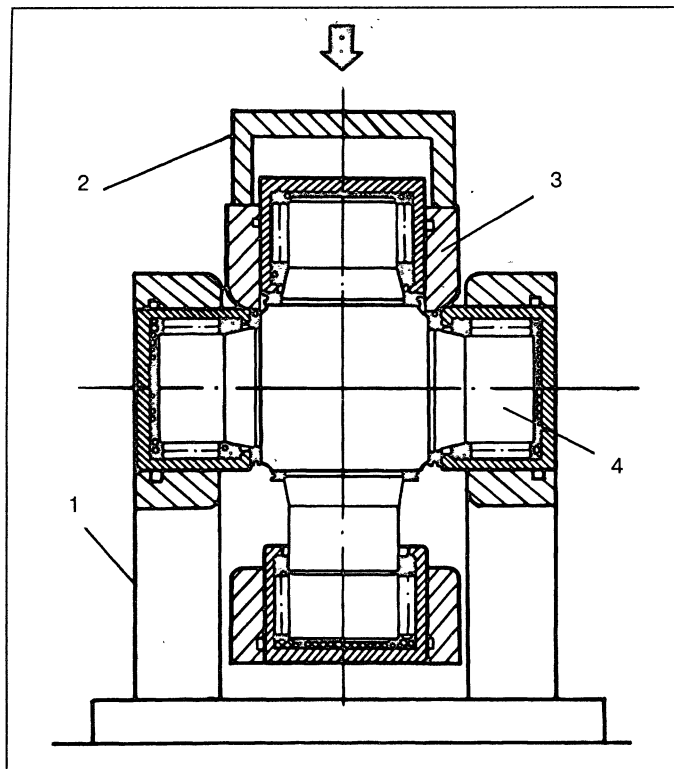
Разборка карданного шарнира: 1 – опора пресса; 2 – втулка; 3 – вилка шарнира; 4 – крестовина
